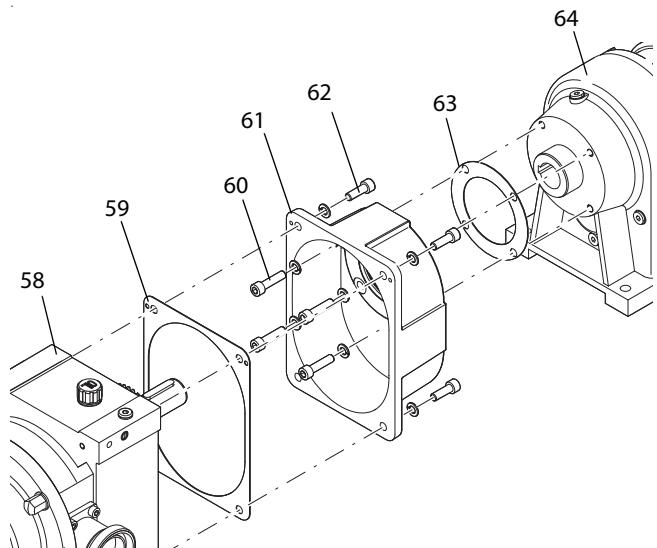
Монтаж редукторного двигателя для конструктивного типа ε ε
